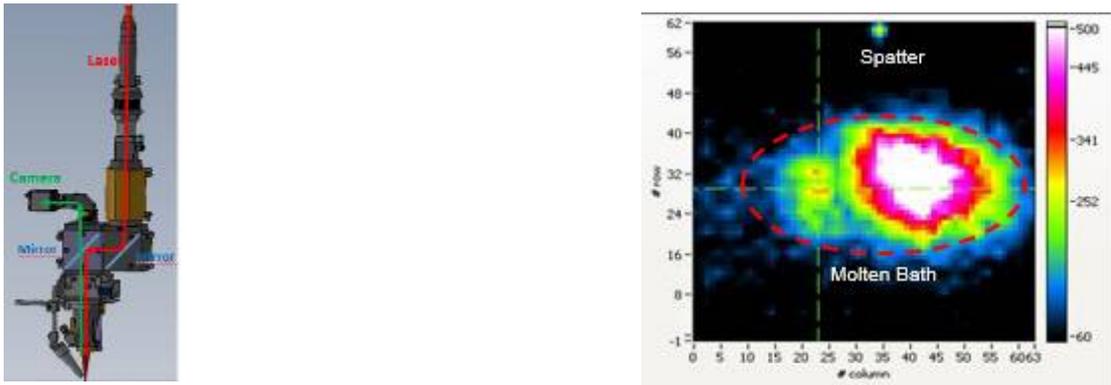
Exemplo de configuração para deteção de defeitos em soldadura a laser com sensores de IR e imagem de monitorização adquirida durante o processo de soldadura - projeto LASHARE LASPRO, Laser equipment ASsessment for HighimpActinnovation in themanufactuRingEuropeanindustry, Grant agreementnumber: 609046
